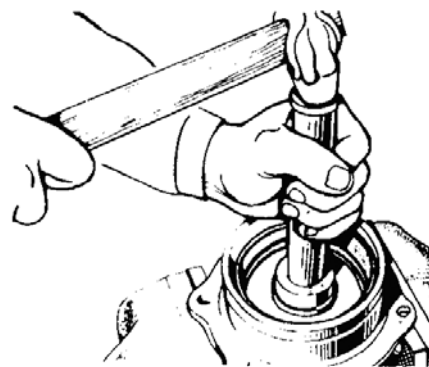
Выпрессовка внешних обойм из стакана подшипников редуктора конечной передачи.
